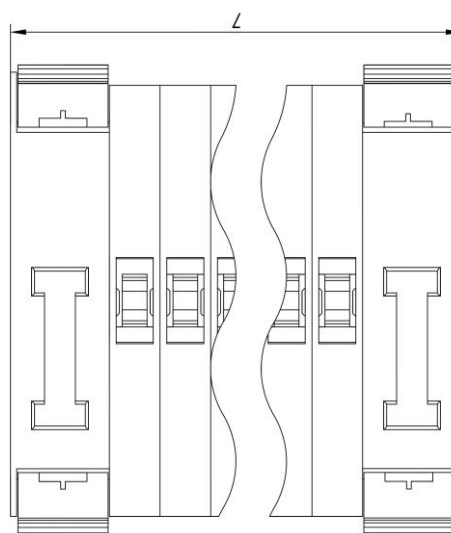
Общий вид рабочей крышки ЭПК. Вид сзади.
